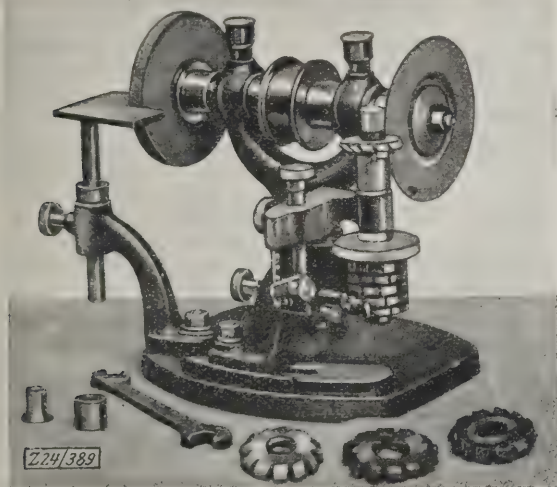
Fräzerschleifmaschine, Bauart Koepfer.
